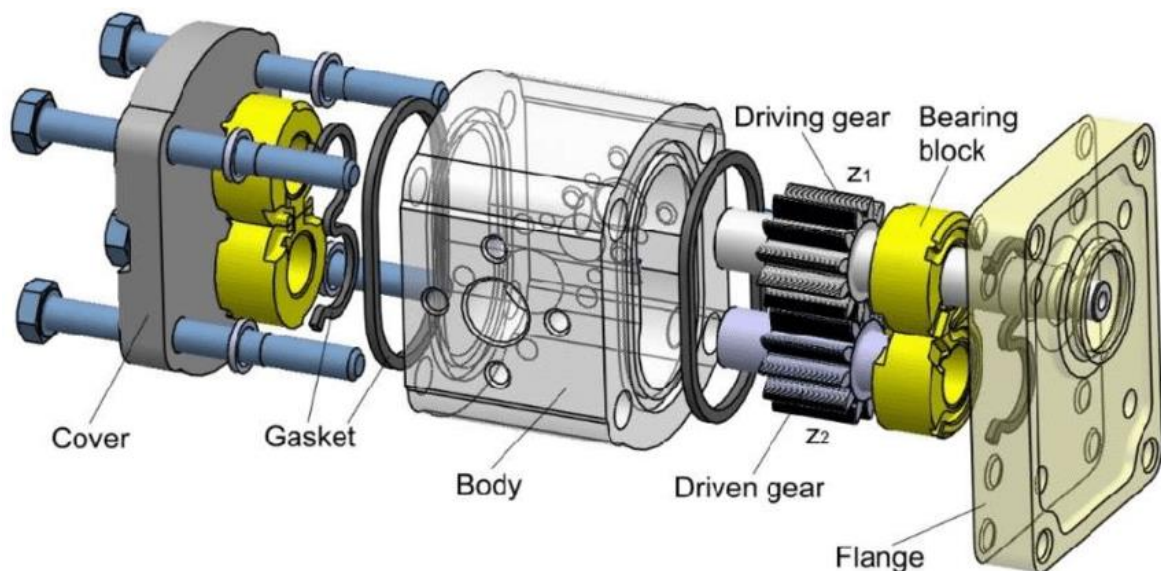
Vista explosionada del despiece de una bomba hidráulica de engranajes (fuente: Internet)
